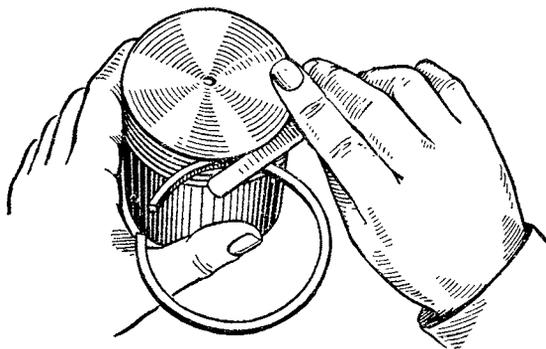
Проверка бокового зазора между поршневым кольцом и канавкой в поршне
